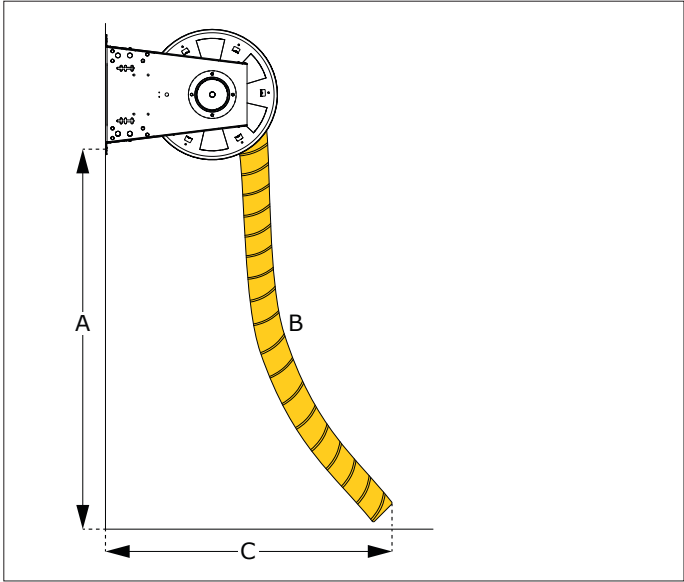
Reichweite und Montagehöhe des Schlauchaufrollers
